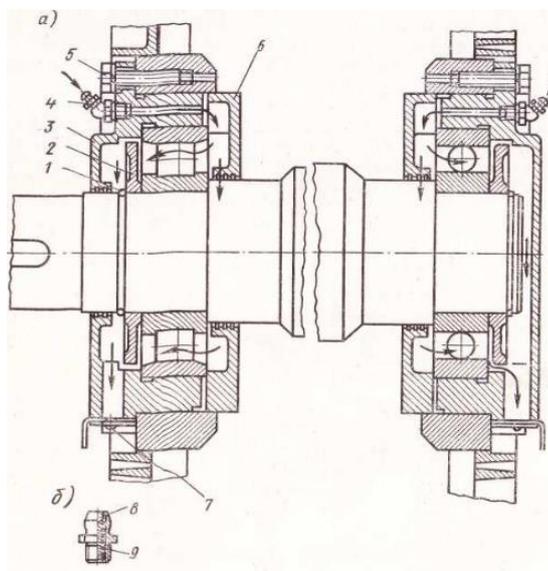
Конструкция подшипникового узла с устройством для пополнения смазки без разборки двигателя (а) и пресс-масленка (б)
